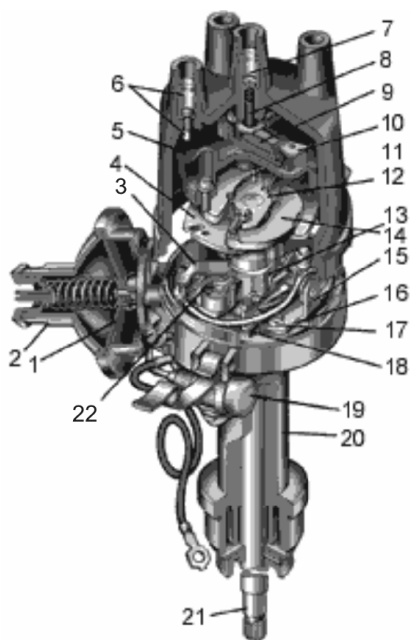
Прерыватель-распределитель: 1 – диафрагма вакуумного регулятора; 2 – корпус вакуумного регулятора; 3 – тяга; 4 – опорная пластина; 5 – ротор распределителя («бегунок»); 6 – боковой контакт крышки; 7 – центральный контакт крышки; 8 – контактный уголек; 9 – резистор; 10 – наружный контакт пластины ротора; 11 – крышка распределителя; 12 – пластина центробежного регулятора; 13 – кулачок прерывателя; 14 – грузик; 15 – контактная группа; 16 – подвижная пластина прерывателя; 17 – винт крепления контактной группы; 18 – паз для регулировки зазоров в контактах; 19 – конденсатор; 20 – корпус прерывателя-распределителя; 21 – приводной валик; 22 – фильтр для смазки кулачка.
